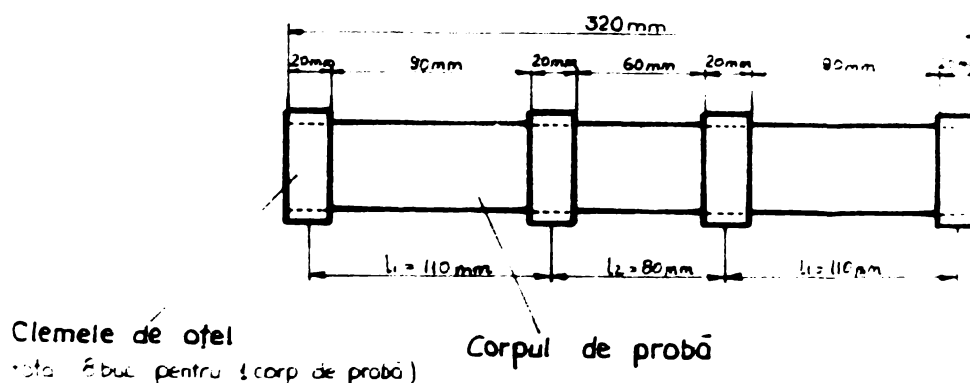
Epruvetă pentru încercare la oboseală, montarea elementelor
